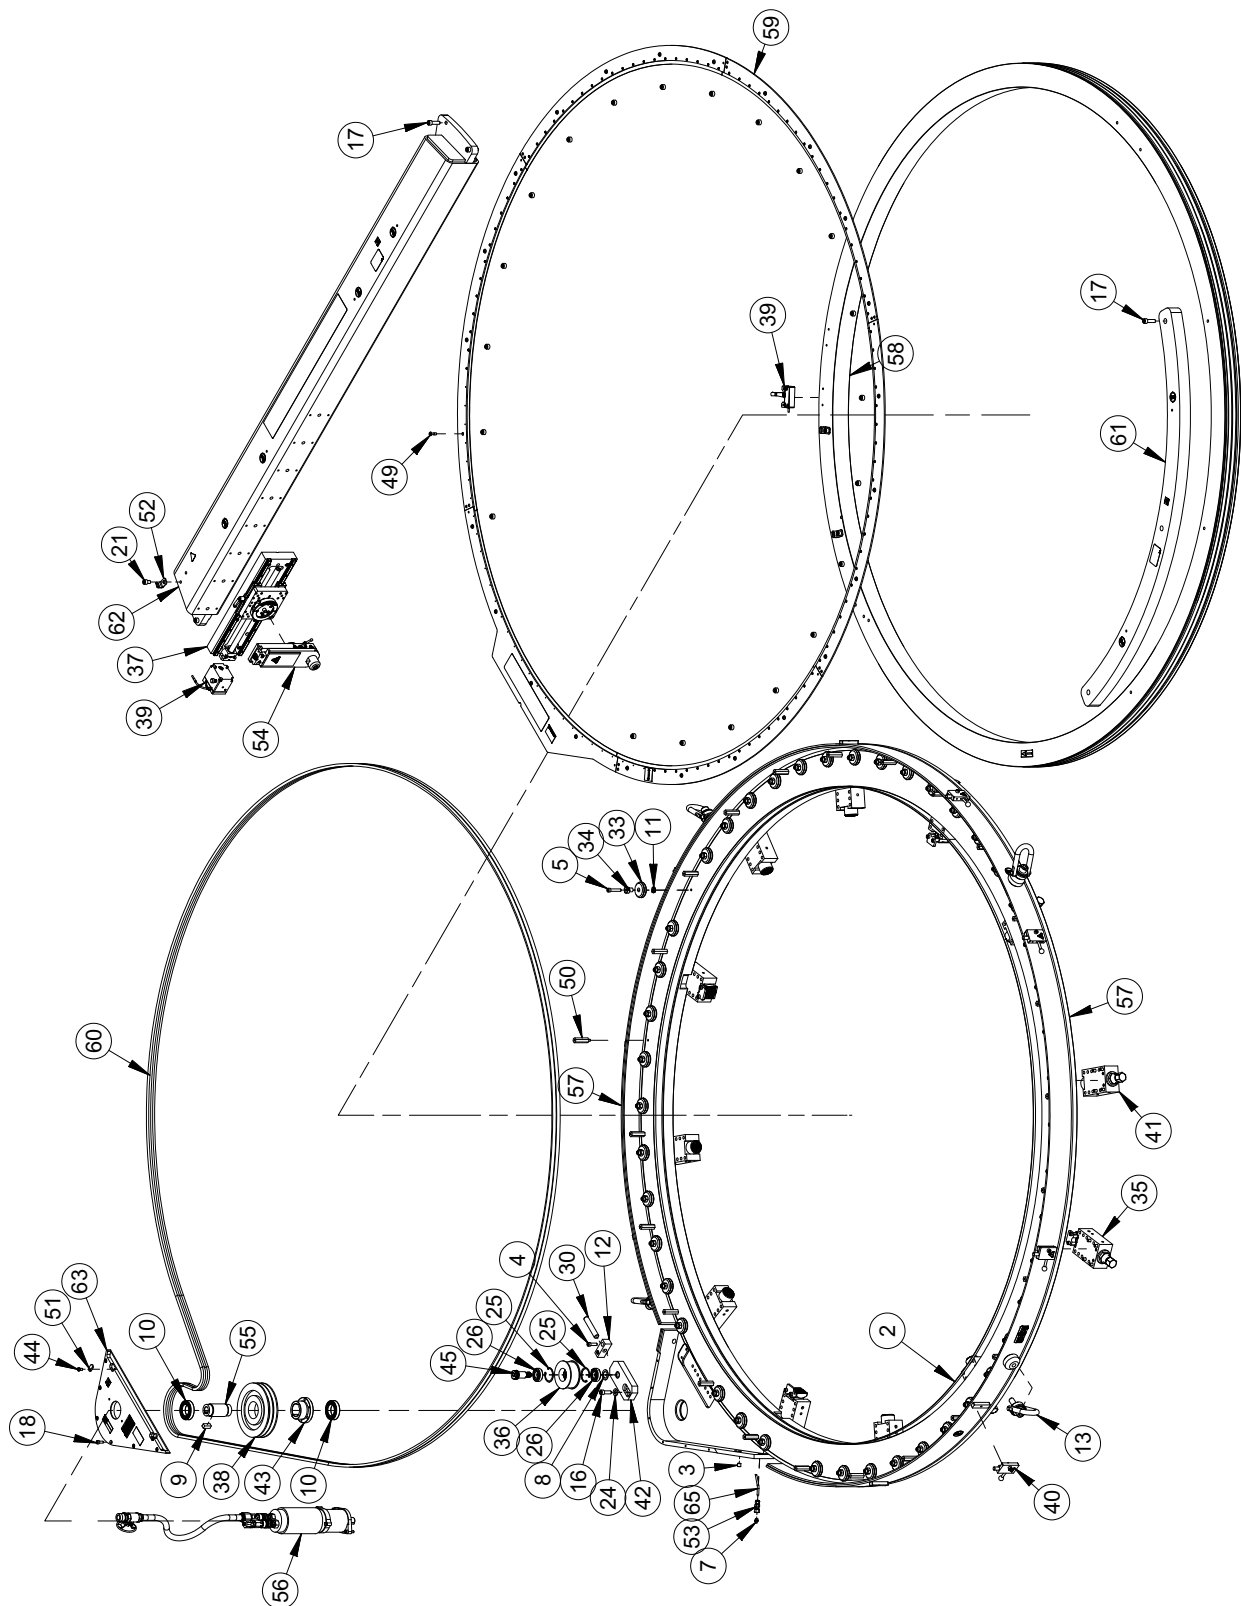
ODF100 SPEED FACER в сборе 1 (кат. № 94790)
